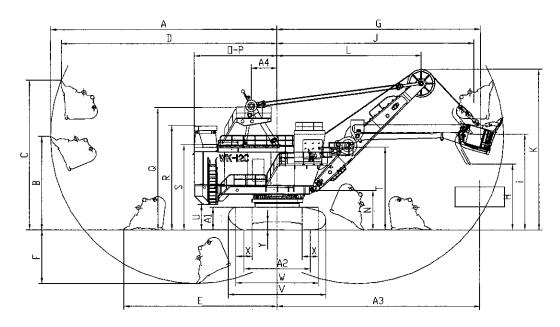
WK-12C 型挖掘机主要工作尺寸和结构尺寸
